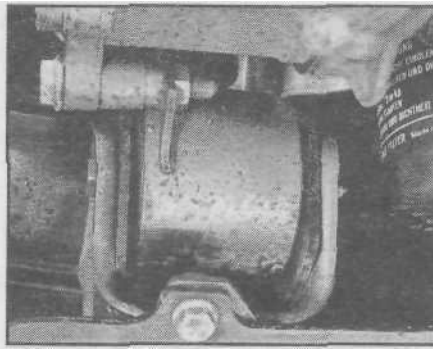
Передняя опора силового агрегата - вид снизу двигатель объемом 1.8 литра
